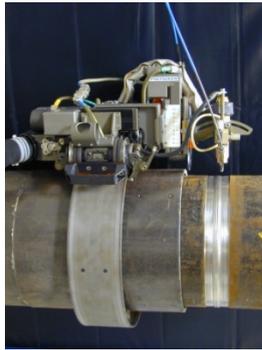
Schweißfahrwerk Polycar MP mit Standardbrenner zum Engspaltschweißen bis 40 mm Wandstärke
